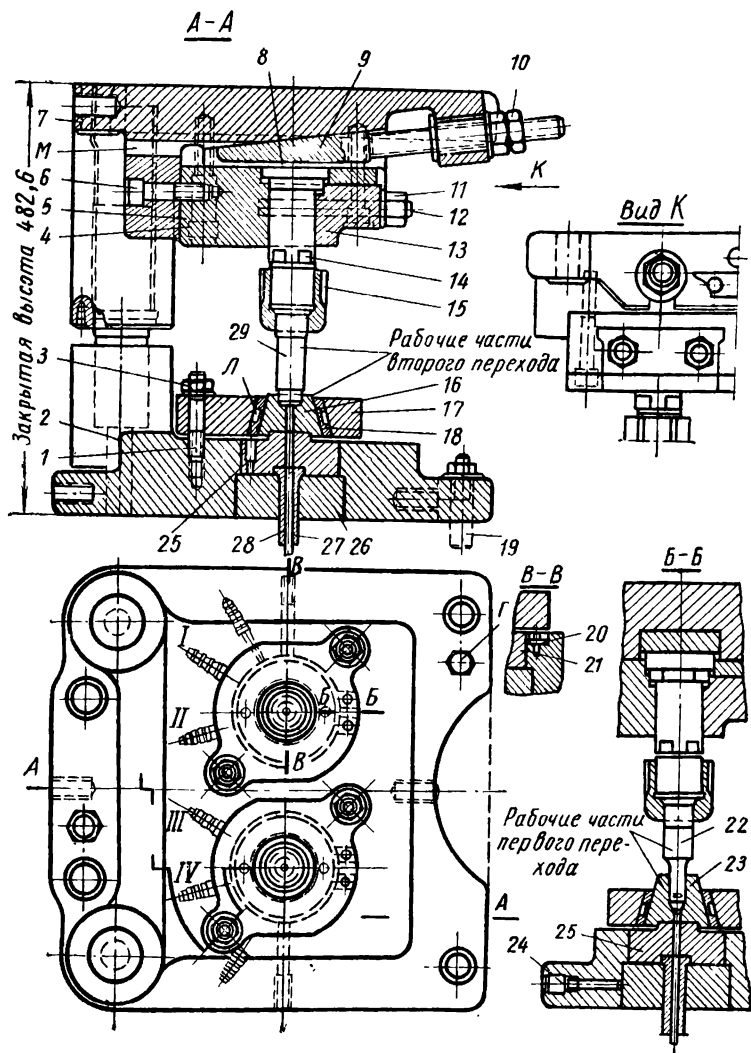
Штамп для выдавливания поковки клапана: 1 и 12 — шпильки; 2 — нижний башмак; 3, 10 и 11 — гайка; 4 и 6 — винты; 5 — державка пуансонов; 7 — верхняя плита; 8 — прокладка; 9 — клин; 13 — зажимная накладка; 14 — пуансонодержатель; 15 — гайка специальная; 16 — матрица окончательного перехода; 17 — зажимное кольцо; 18 — водяная рубашка; 19 — фиксационная шпилька; 20 — фиксационный сухарь; 21 — стакан направляющий; 22 — пуансон первого перехода; 23 — матрица первого перехода; 24 — болт стопорный; 25 — направляющий стакан; 26 — опорная шайба; 27 — выталкивающая шпилька; 28 — направляющая втулка шпильки; 29 — пуансон окончательного перехода
